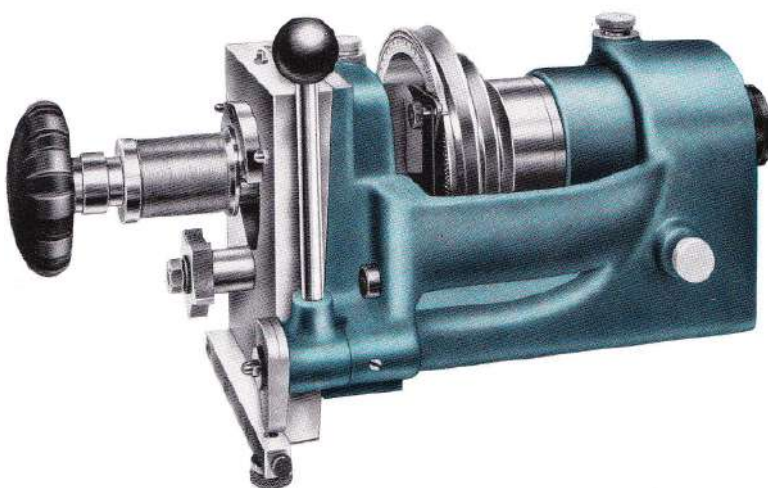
Sliding-spindle screw-cutting headstock*, [9].
